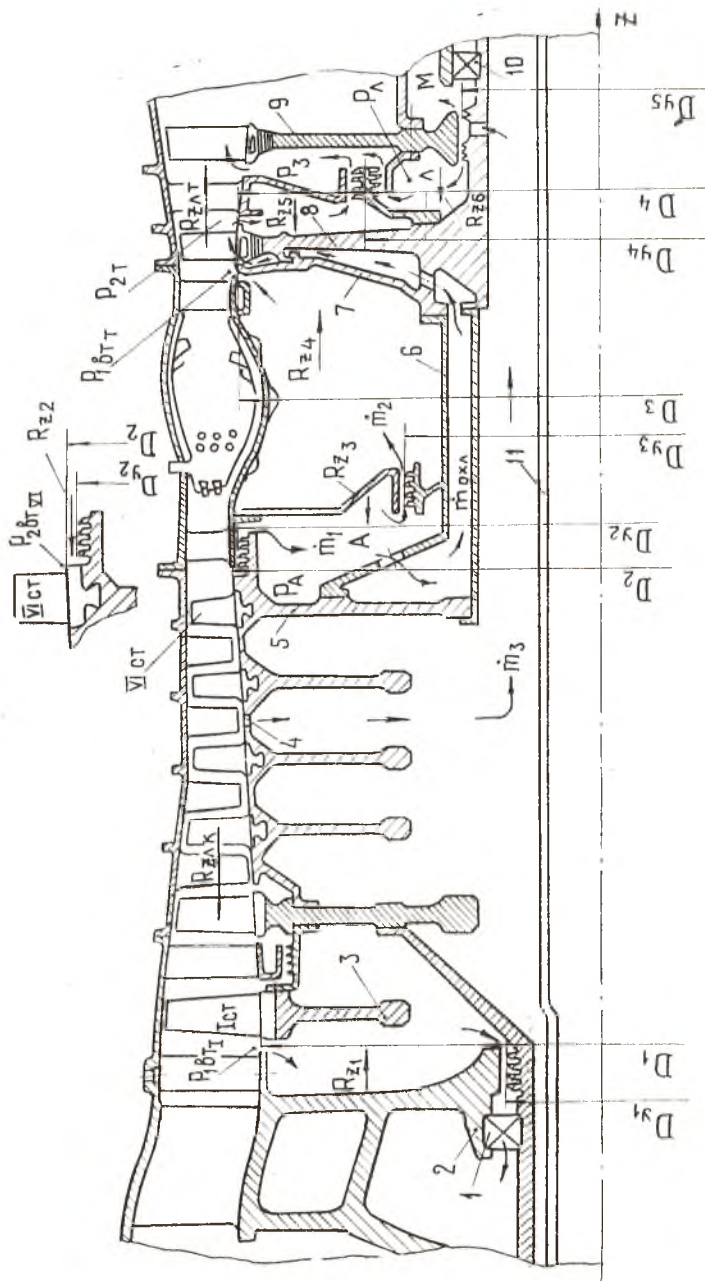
К расчету системы разгрузки опоры ротора турбокомпрессора ГТД от осевого усилия как задачи нелинейной оптимизации: 1 — радиально-упорный подшипник; 2 — корпус опоры; 3 — диск первой ступени компрессора; 4 — отверстие для отбора воздуха; 5 — диск последней ступени компрессора; 6 — соединительный вал; 7 — диск дефлектора; 8 — диск турбины внутреннего каскада ТК; 9 — диск турбины внешнего каскада ТК; 10 — радиальный подшипник; 11 — вал ТК внешнего каскада
